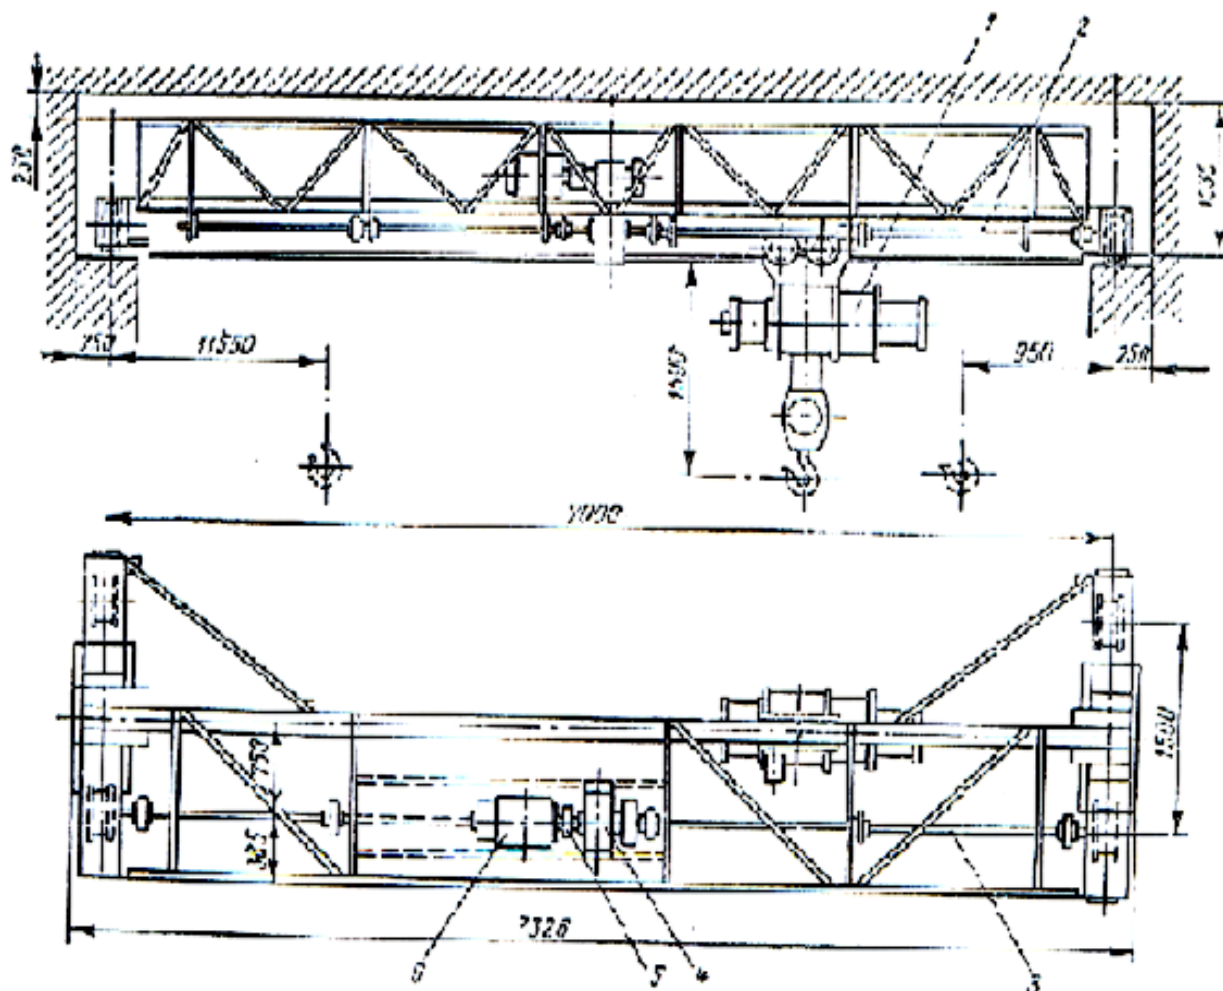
Общий вид однобалочного мостового крана опорного типа сварной конструкции:
